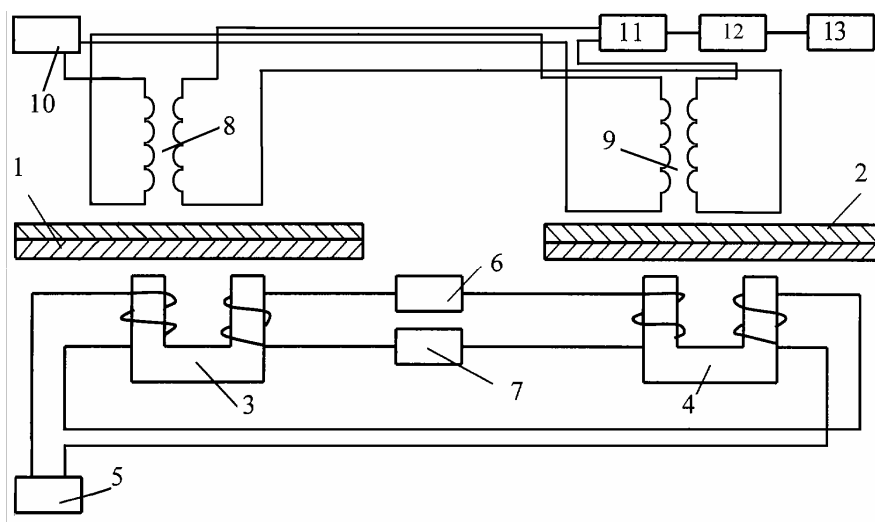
Схема устройства, реализующая способ непрерывного контроля толщины и сплошности соединений слоев биметалла:
